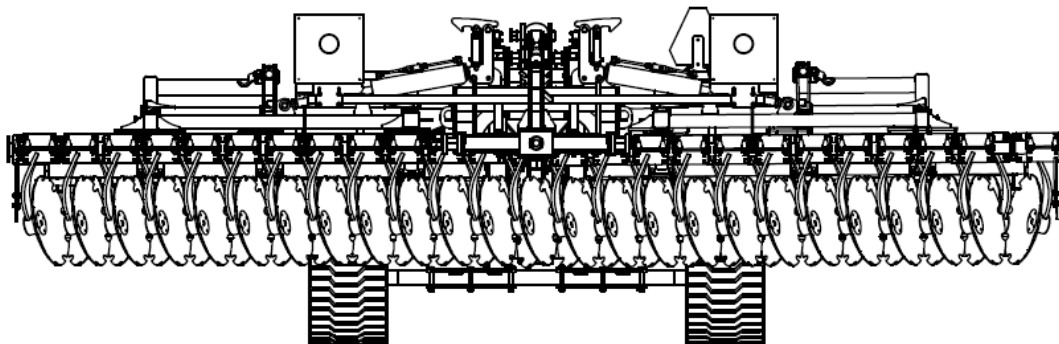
Vue de la machine à la fin de la séquence d'ouverture des ailes. Les bras de la machine sont complètement ouverts.
